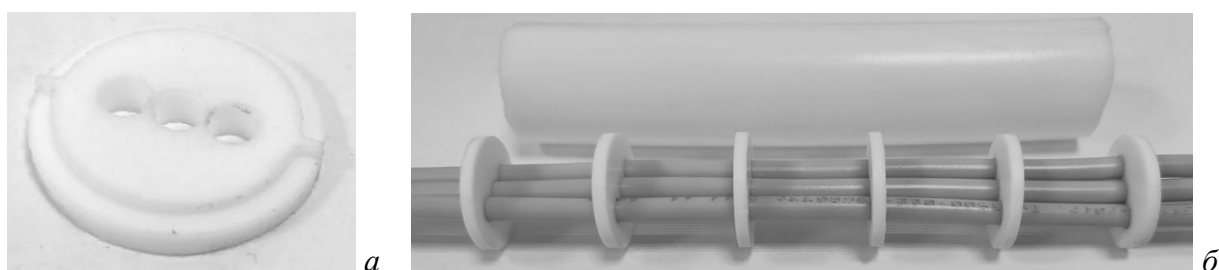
Фторопластовая пластина для крепления проводов (а) и провода, фиксируемые пластинами (б)
